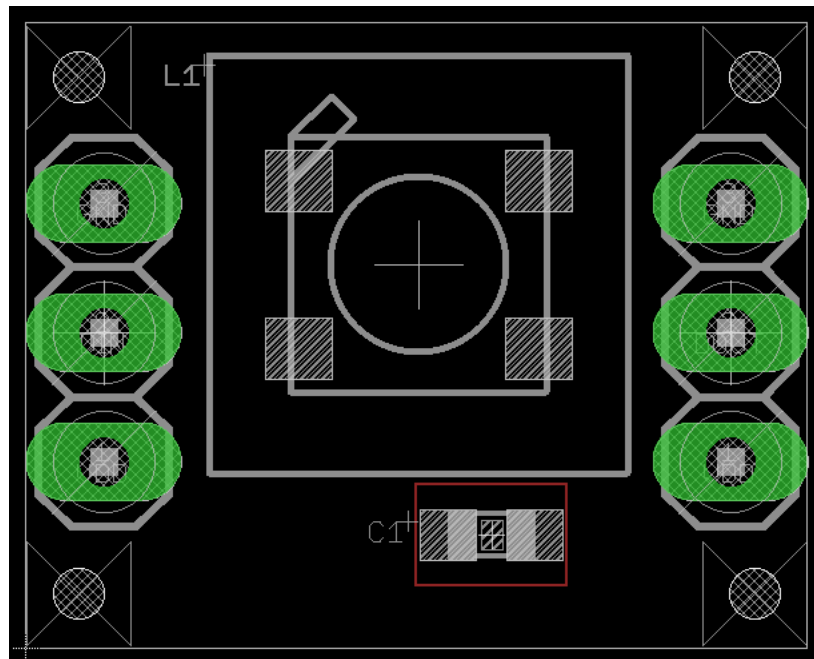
Distribuição dos componentes no *layout* da PCB do LED
